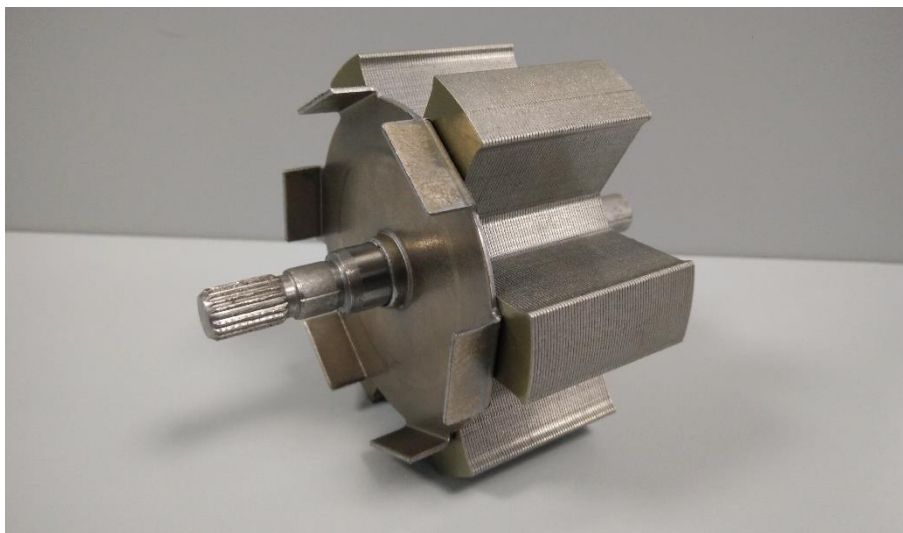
Rotor do motor de relutância variável que equipa a Yämmi 2.
